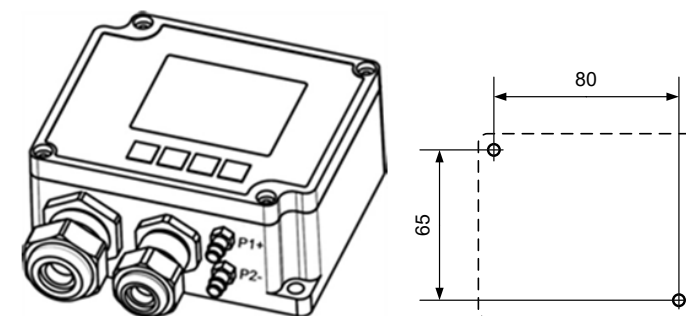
Вид корпуса изделия и разметка отверстий для крепления
